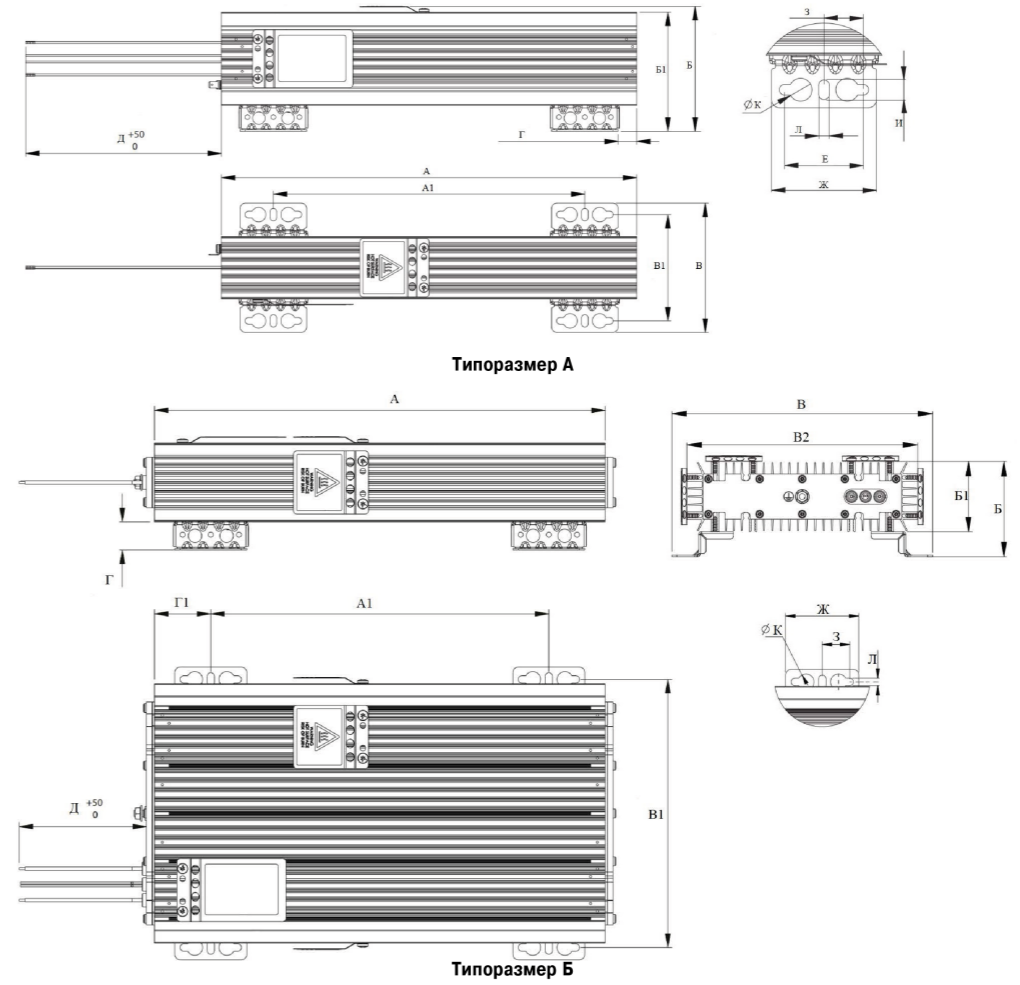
Габаритно-установочный чертеж резисторов серии РБ4
